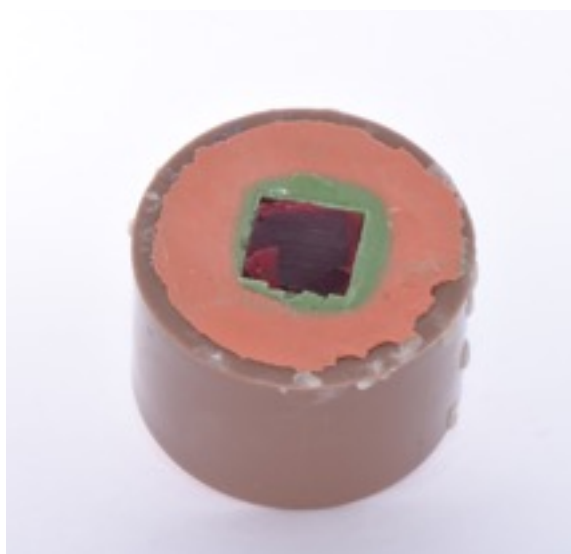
Moldagem do bloco mestre de poliuretano impresso.
